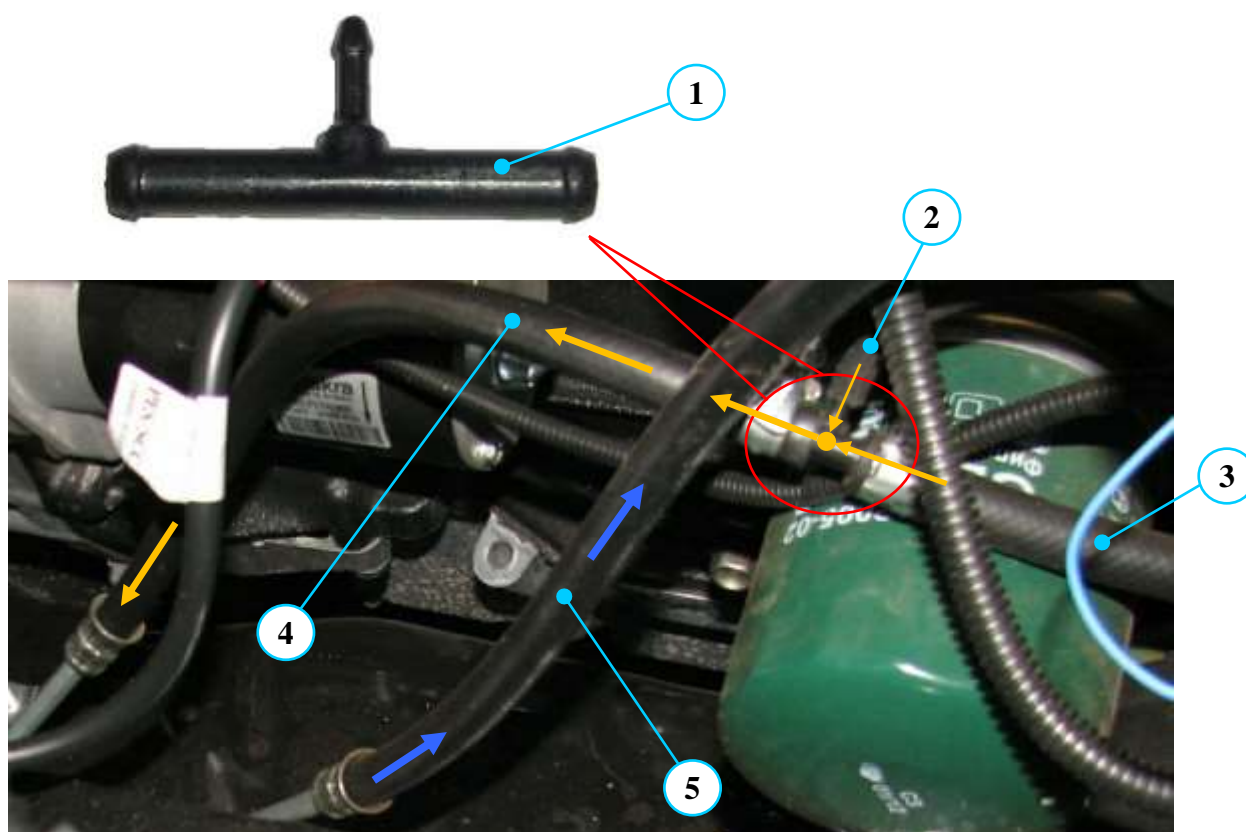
Внешний вид и место установки тройника для слива отсечного топлива из ТНВД и топливных форсунок в топливный бак:
